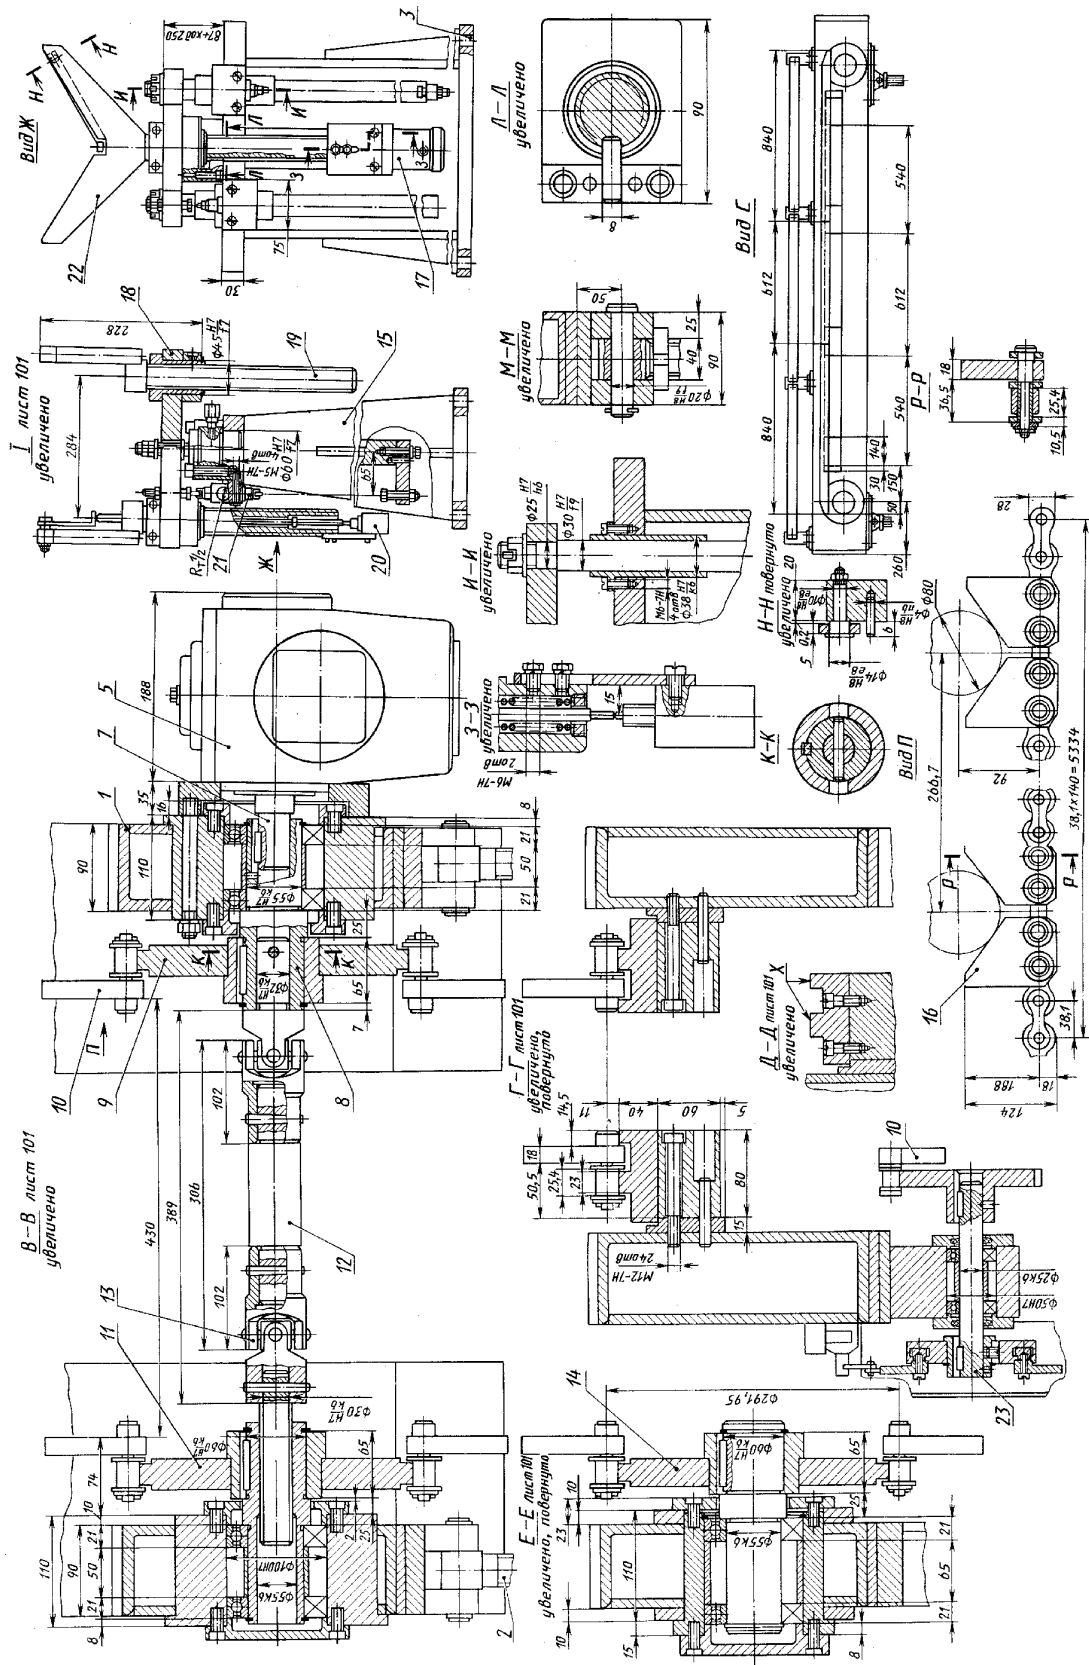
Автоматизованый накопичувальний пристрій для заготовок і деталей (механізми приводів)
